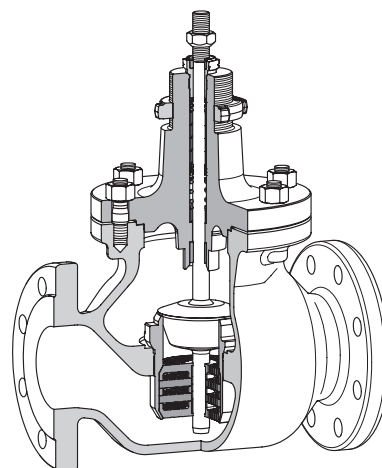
· Клапан тип 3251 с гарнитурой AC-2 Trim и четырьмя дроссельными шайбами
